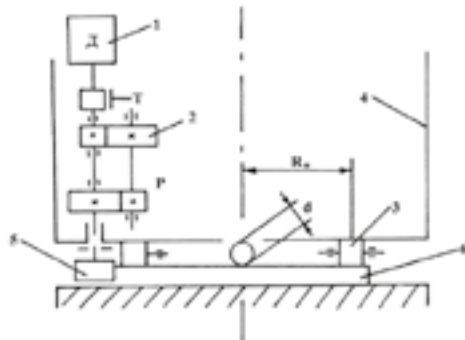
а – Механізм повороту екскаватора (кінематична схема)
